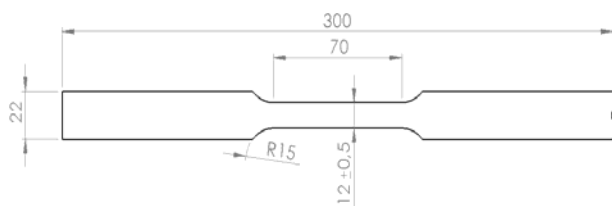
Corpos de prova para ensaio de tração (Adaptado de ASTM E21-05, 2013)
